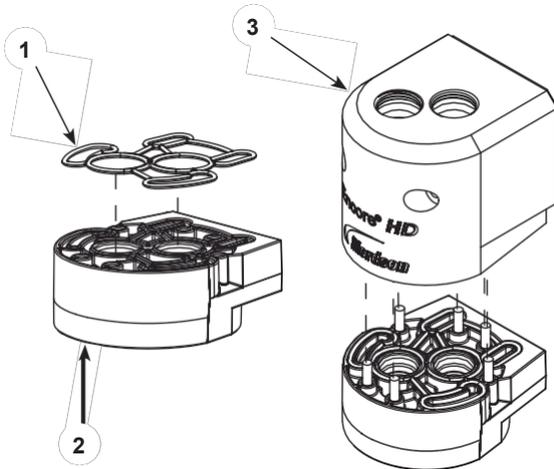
Assemblage du bloc Y inférieur au collecteur de purge
